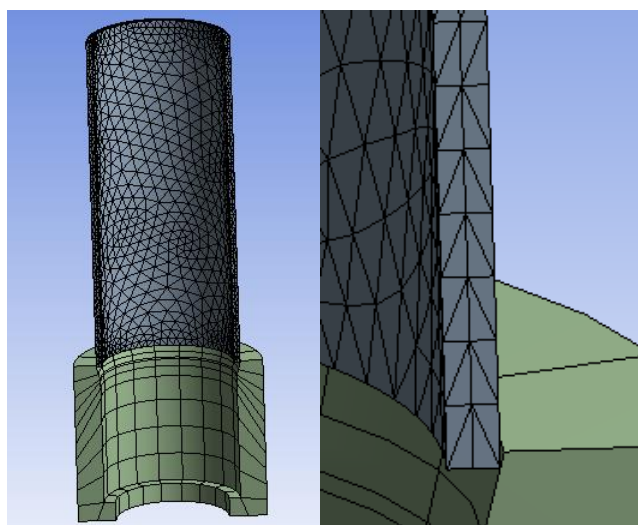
Схема разбиения заготовки на конечные элементы
